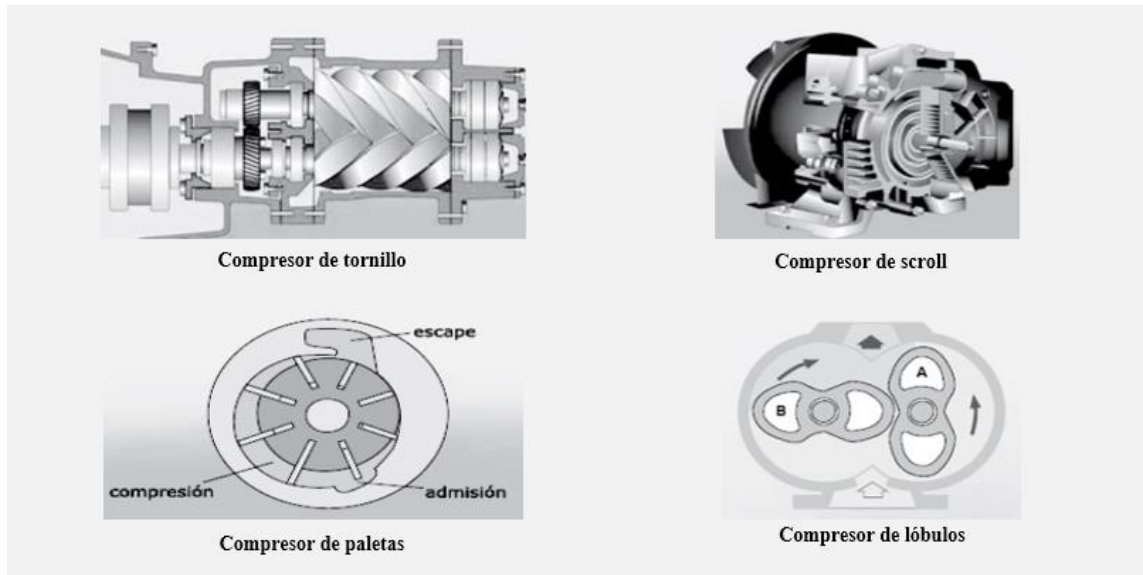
Compresores de desplazamiento positivo. Fuente: Junta de Castilla y León
